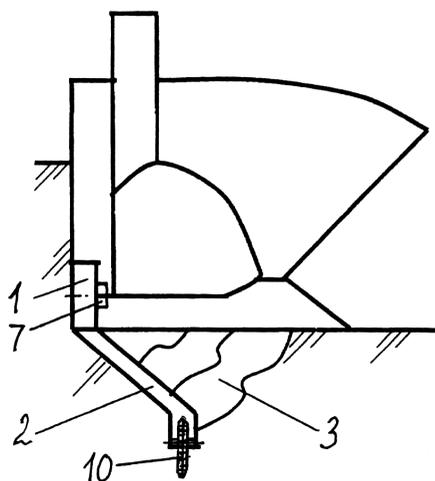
Общий вид корпуса плуга (вид спереди)
